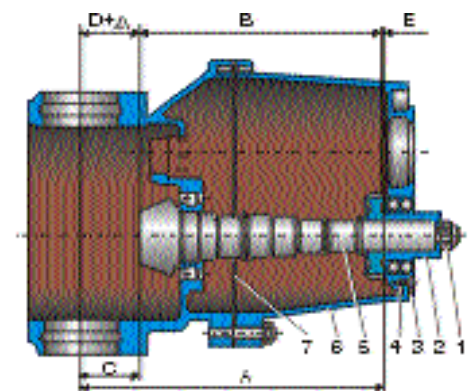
Установка ведущей шестерни при определении монтажного размера С: 1 – гайка; 2 – ведомая шестерня пятой передачи или технологическая втулка; 3 – пластина крепления подшипников; 4 – винт; 5 – подсобранная ведущая шестерня главной передачи; 6 – картеры в сборе; 7 – прокладка
